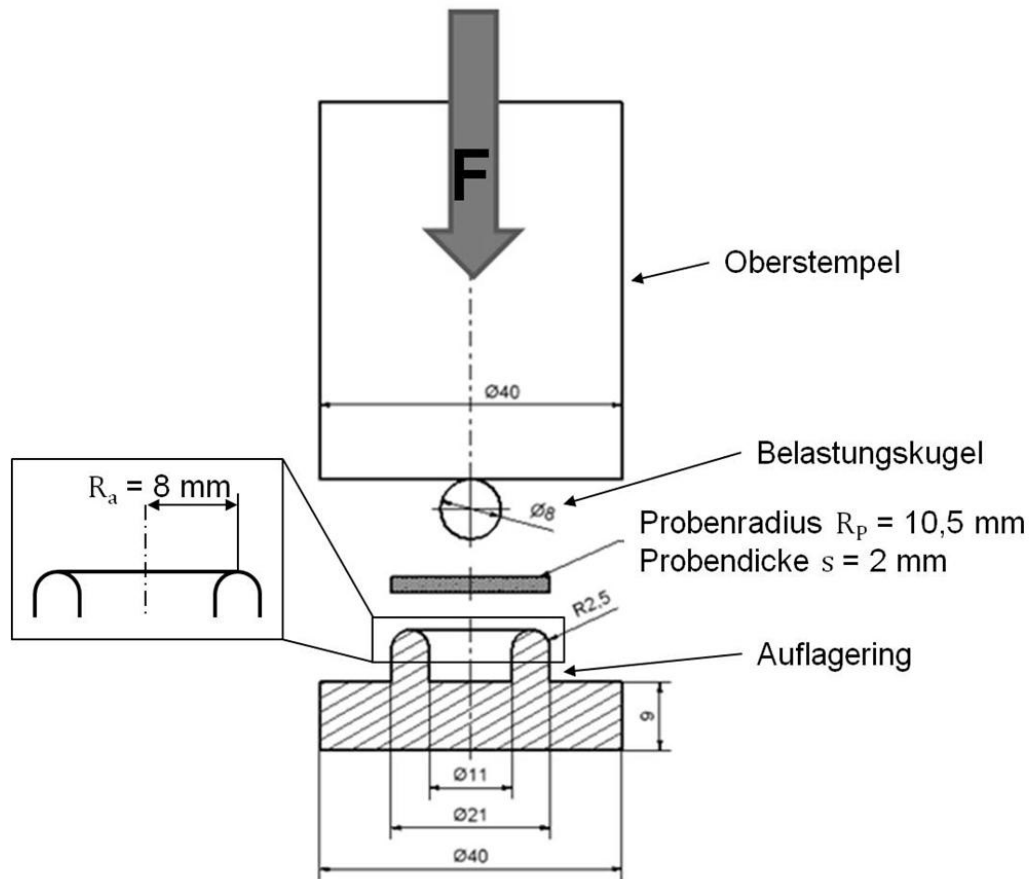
Aufbau des Ball-on-Ring-Tests mit Angabe der Proben- und Prüfeinrichtungsabmessungen. Prüfeinsatz für Universalprüfmaschinen.
